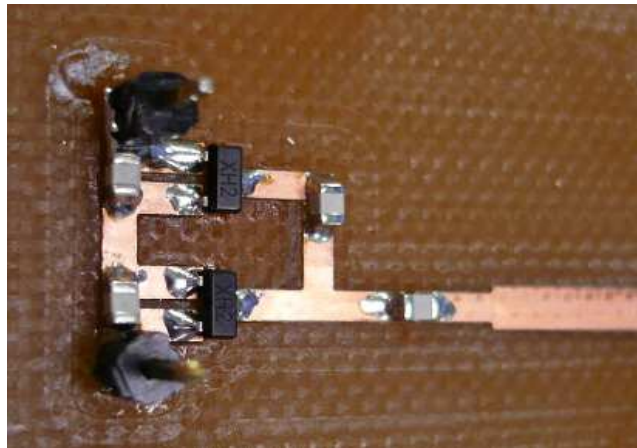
Pistas del circuito rectificador con los componentes soldados.
